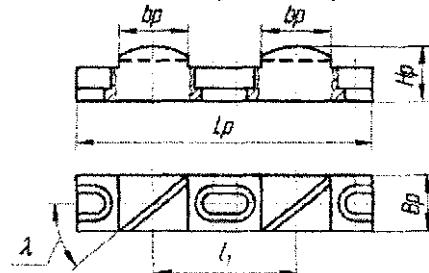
Конструкция резца-зуба развертки со сдвоенными безвершинными зубьями
